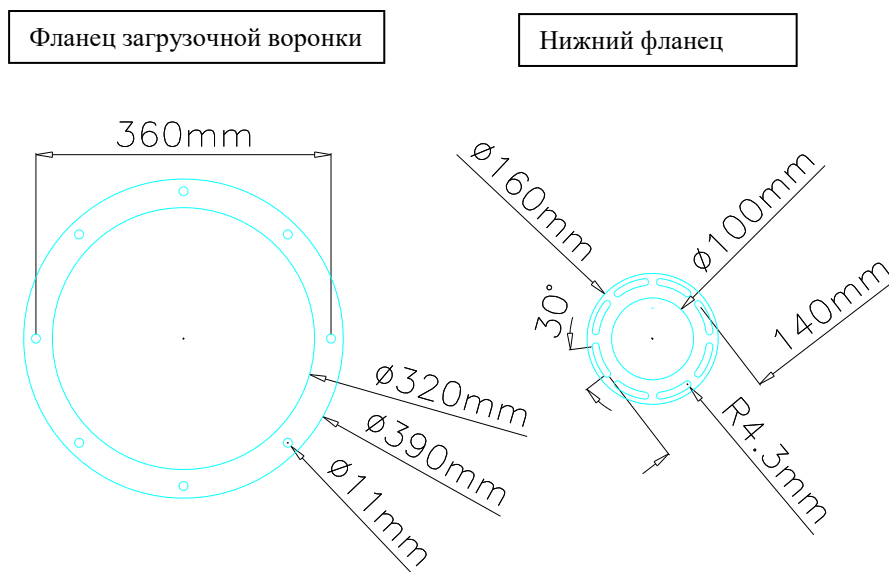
Фланец загрузочной воронки и нижний фланец для CD400/CD800
